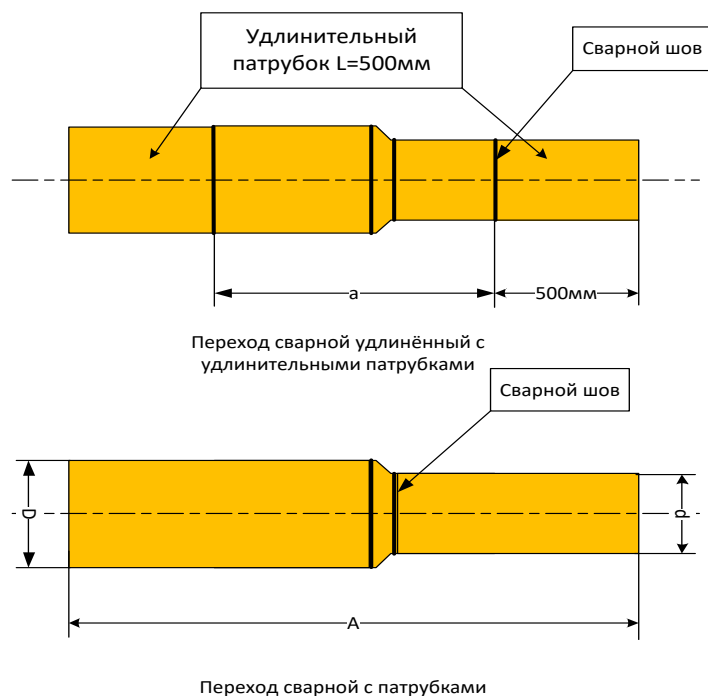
Варианты исполнения соединений полиэтиленовых труб и фитингов (переход сварной удлиненный с удлинительными патрубками)
